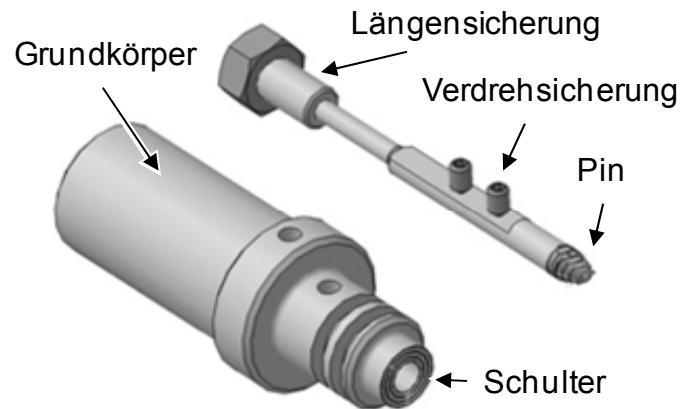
Modular aufgebautes Schweißwerkzeug
